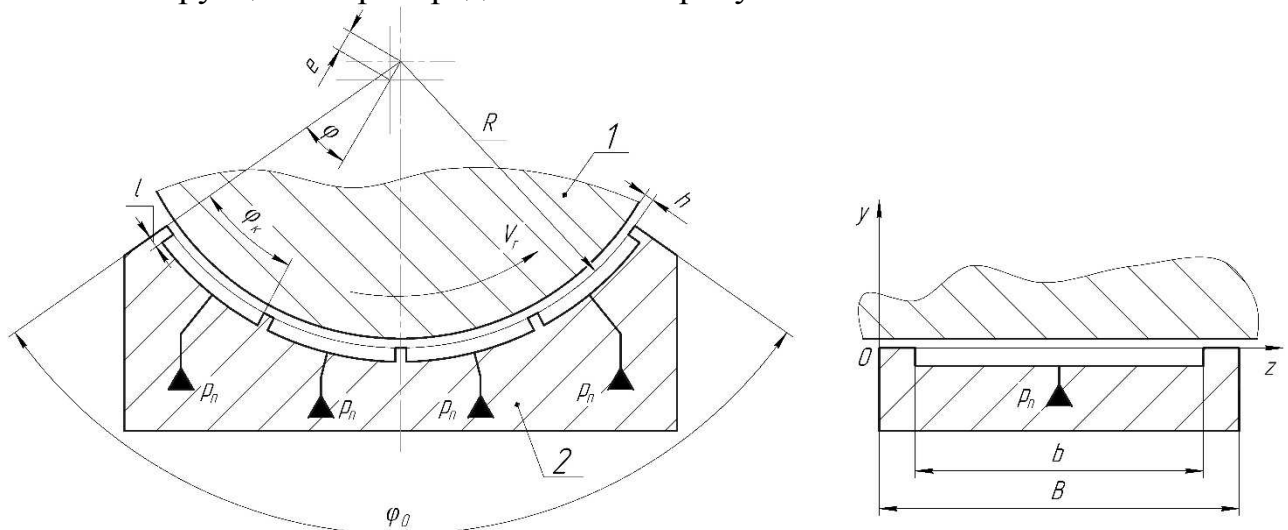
Расчетная схема опоры; 1 – шейка вала ротора; 2 – ГСО
